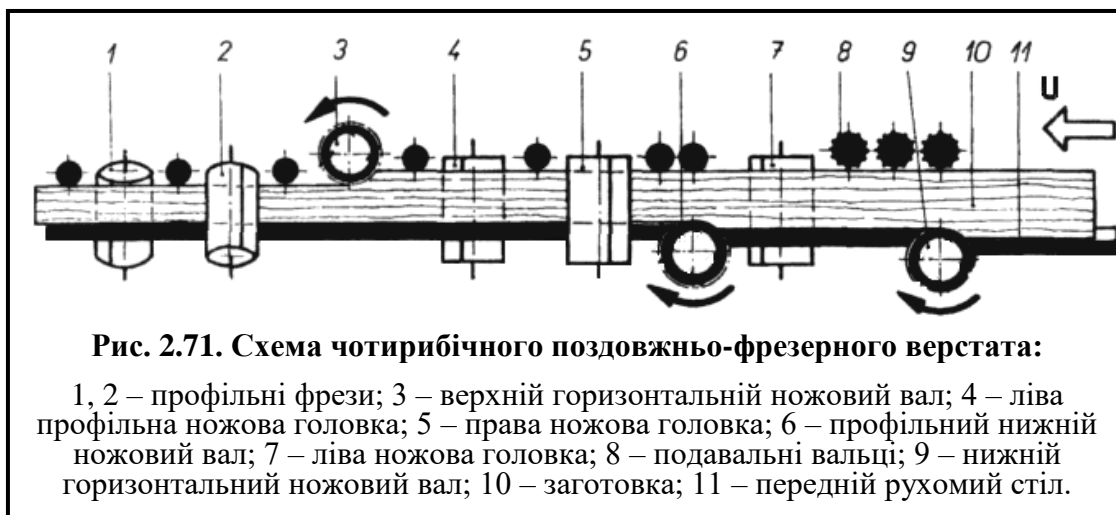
Схема чотирибічного поздовжньо-фрезерного верстата:
